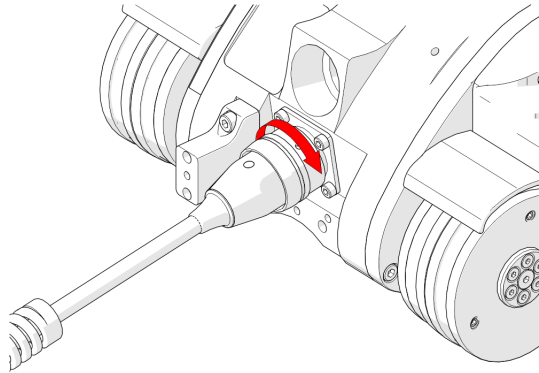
Ausrichten auf die Halterung für die Versorgungsleitung des Fahrwagens
